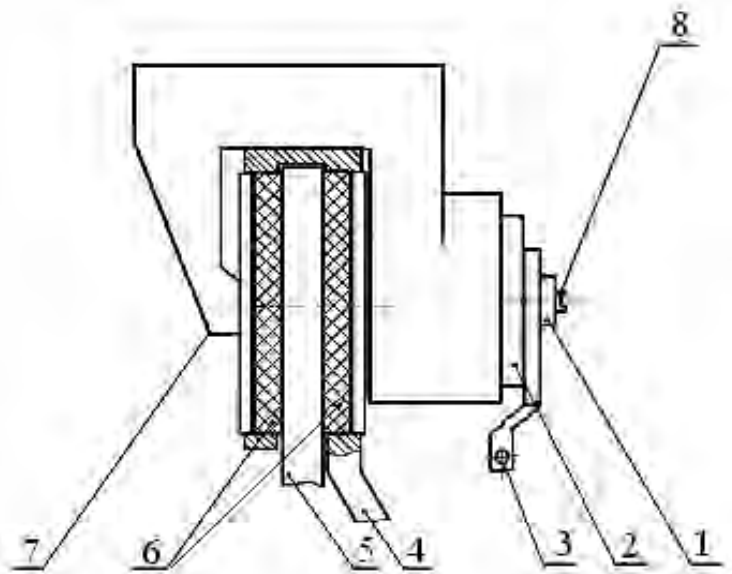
Дисковый тормоз с механическим приводом: 1 – гайка; 2 – механическое нажимное устройство; 3 – рычаг; 4 – корпус; 5 – диск; 6 – колодка; 7 – скоба; 8 – шпилька
